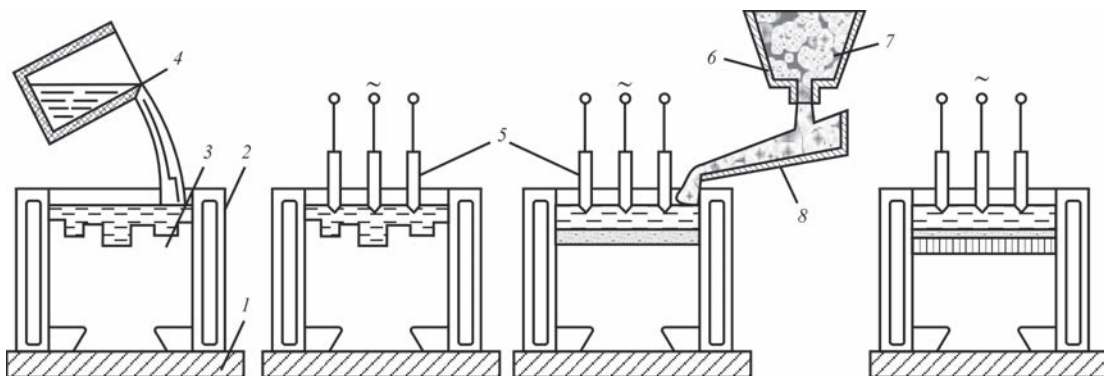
Схема электрошлаковой наплавки изношенных штампов с использованием в качестве присадки стружки штамповой стали: 1 — поддон; 2 — неподвижный кристаллизатор; 3 — изношенный штамп; 4 — ковш с жидким шлаком; 5 — неплавящиеся электроды; 6 — емкость для присадочного материала; 7 — присадочный материал; 8 — желоб
